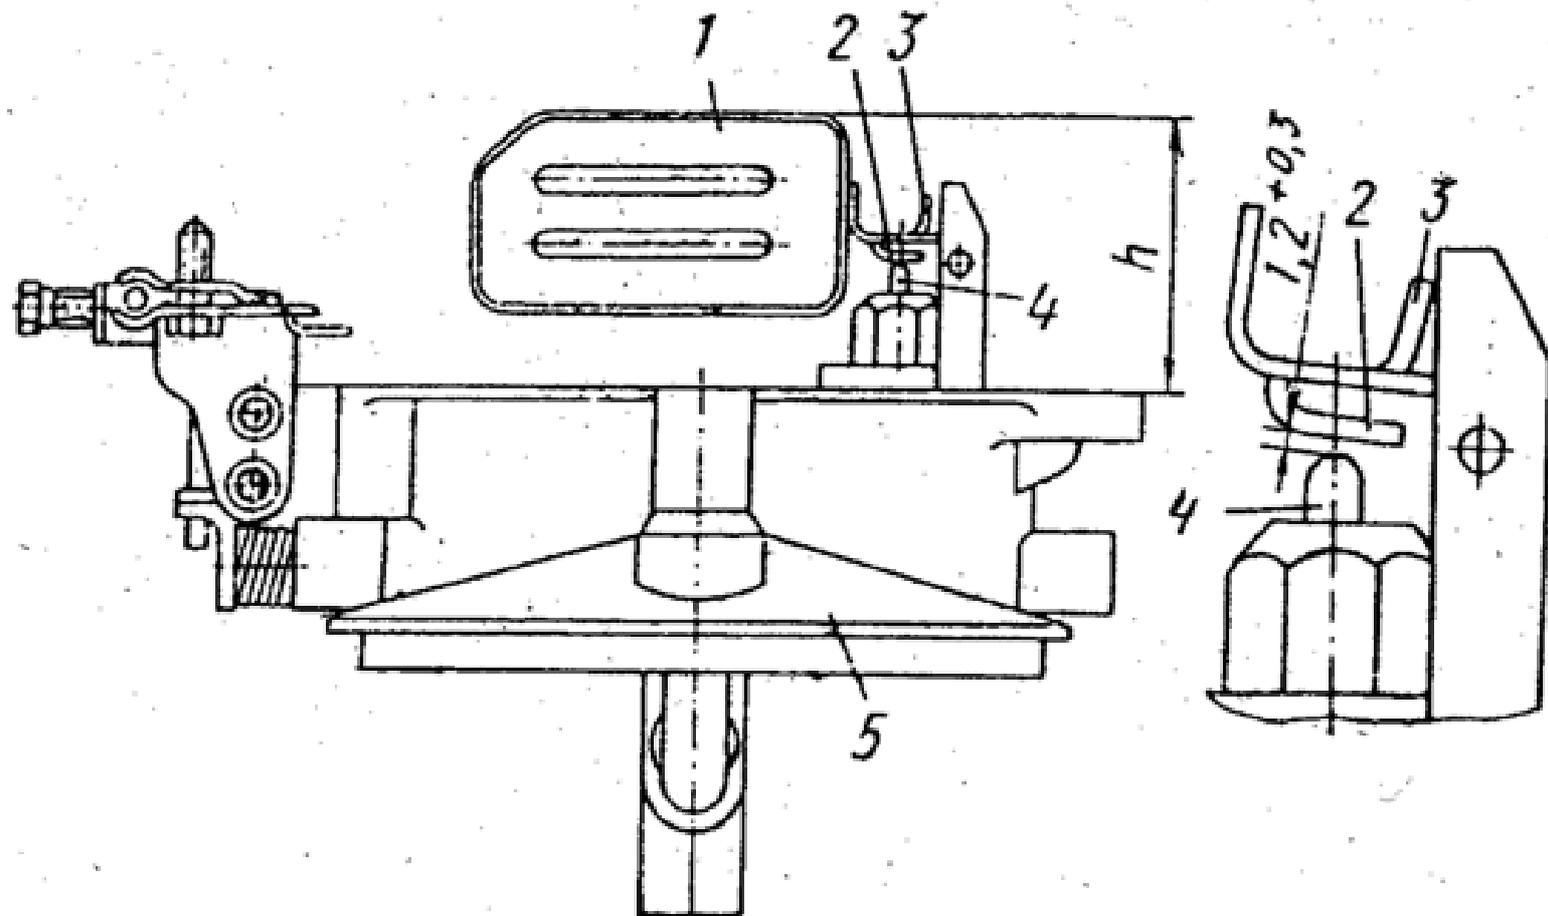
Проверка установки поплавка на крышке поплавковой камеры карбюратора К-126Л: 1 - поплавок; 2 - язычок рычага поплавка; 3 - ограничитель хода поплавка; 4 - клапан подачи топлива; 5 - крышка поплавковой камеры
